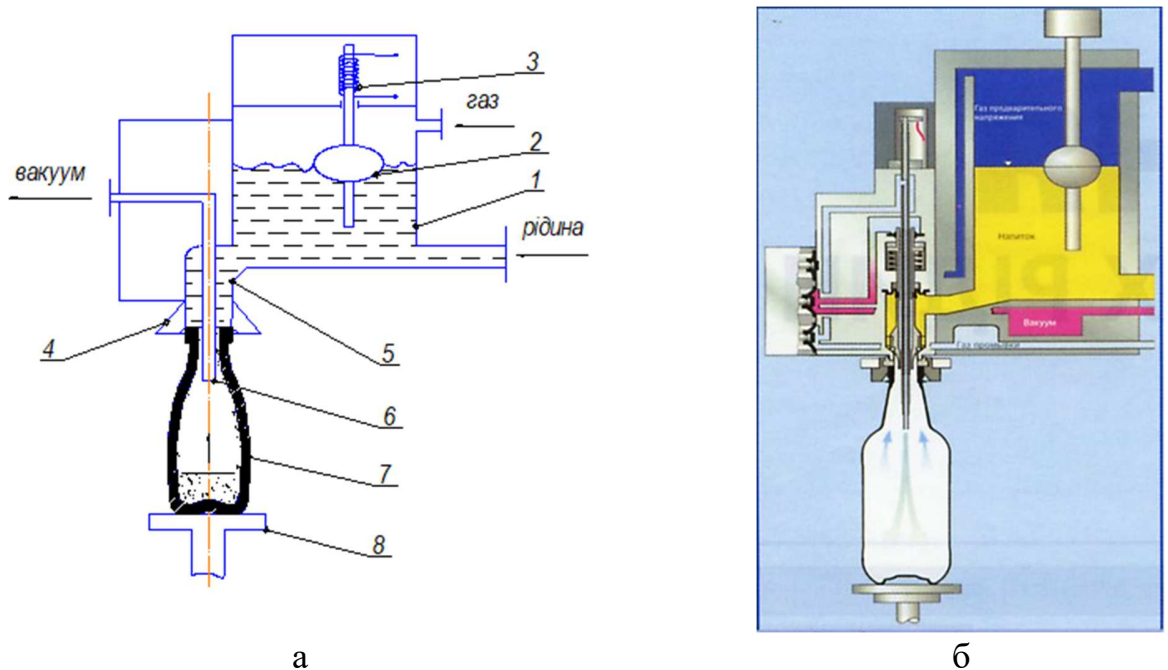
Дозувальний пристрій з індуктивним вимірюванням рівня в резервуарі: а – схема; б – загальний вигляд; 1 – витратний резервуар; 2 – поплавець; 3 – індуктивний датчик; 4 – дзвіночок; 5 – трубка подачі рідини; 6 – трубка відведення повітря; 7 – тара; 8 – стіл подачі тари
